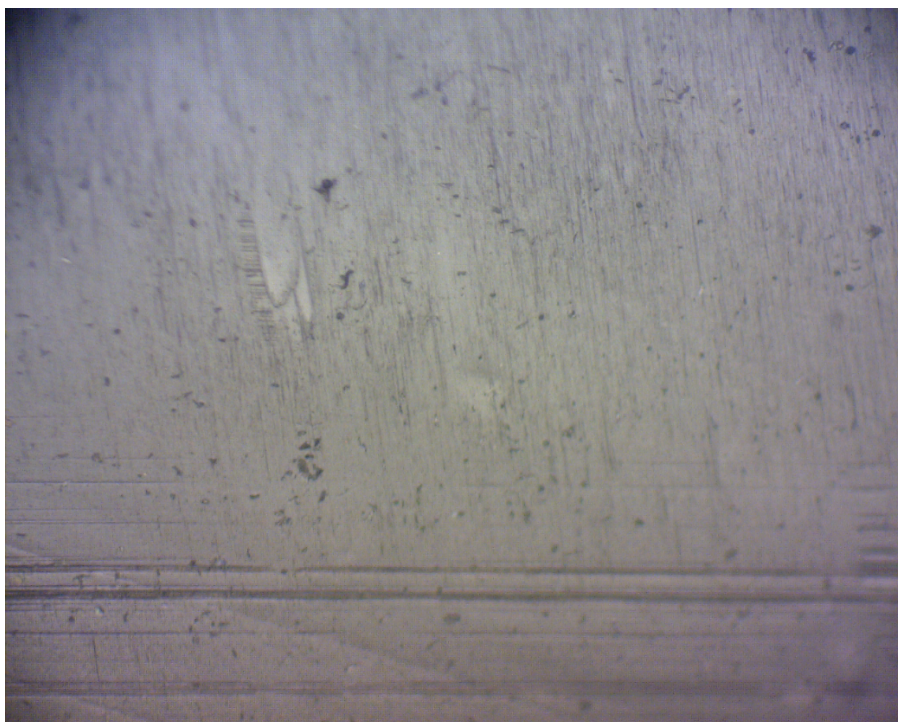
Impressão da superfície depois da aplicação no gearbox da turbina eólica nº 01-14
